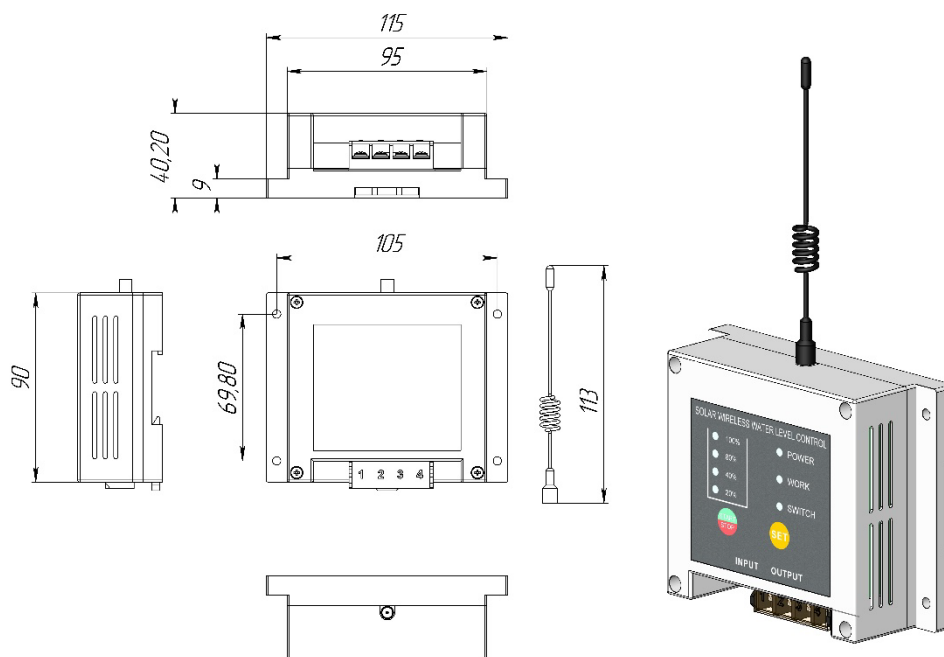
Габаритные размеры контроллера НК-У
